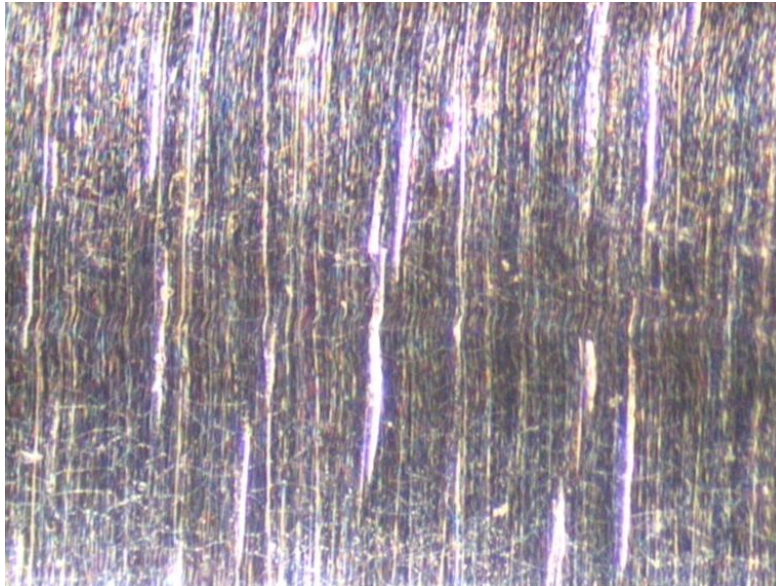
Poloha zápichu – uvolnění výroby u spodní tolerance
